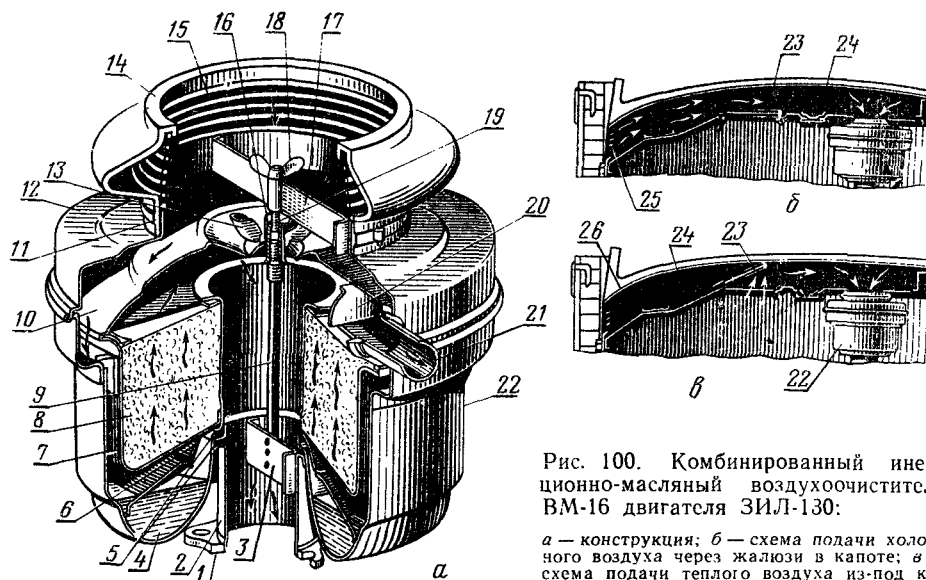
Комбинированный инерционно-масляный воздухоочиститель ВМ-16 двигателя ЗИЛ-130:
